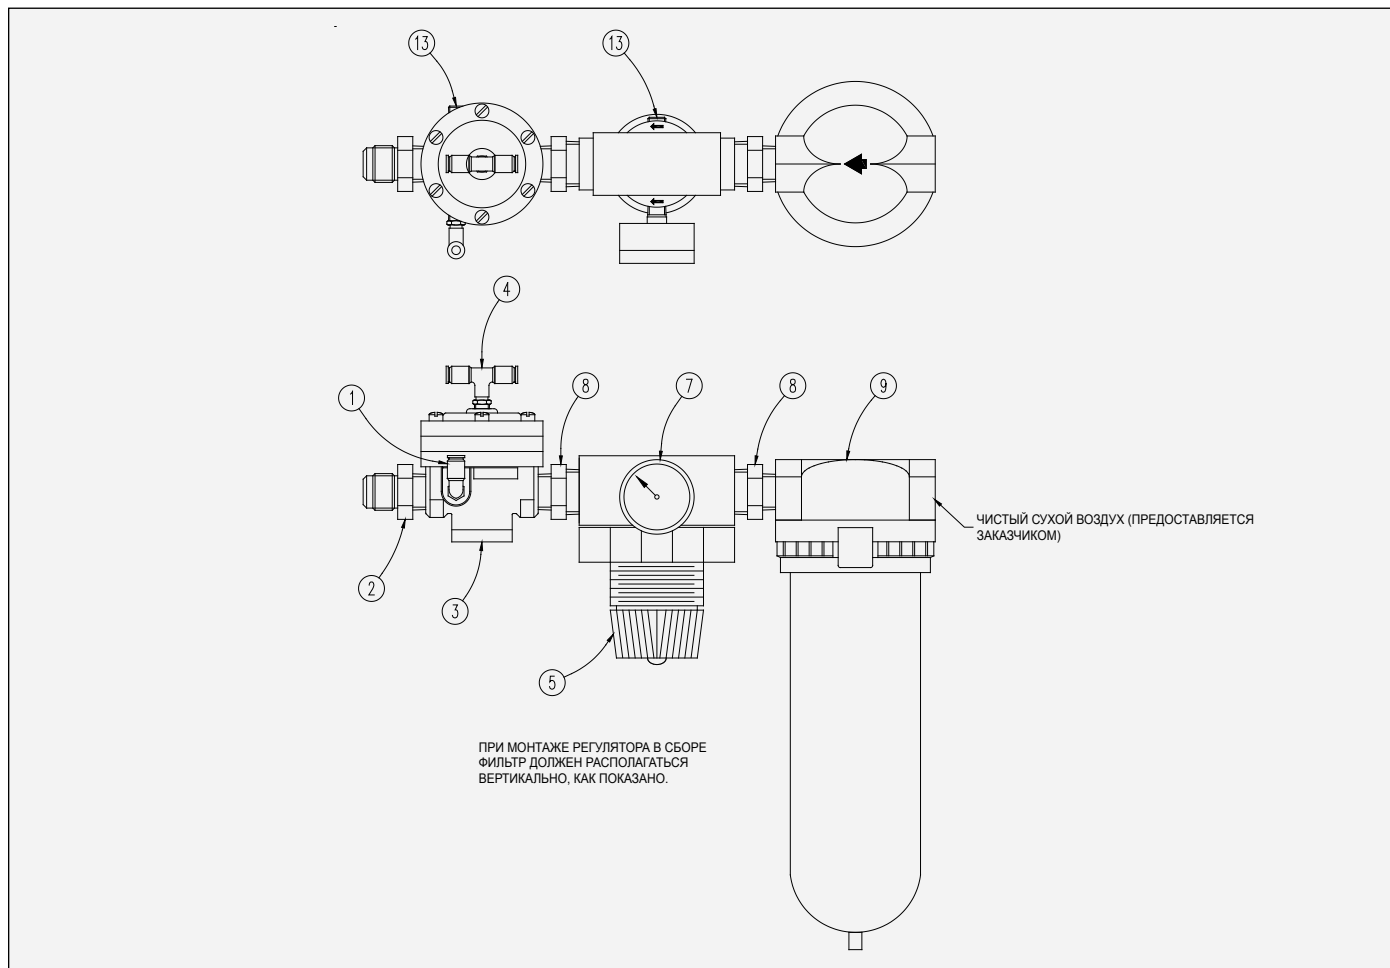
Регулятор воздуха для привода в сборе 78170-00
